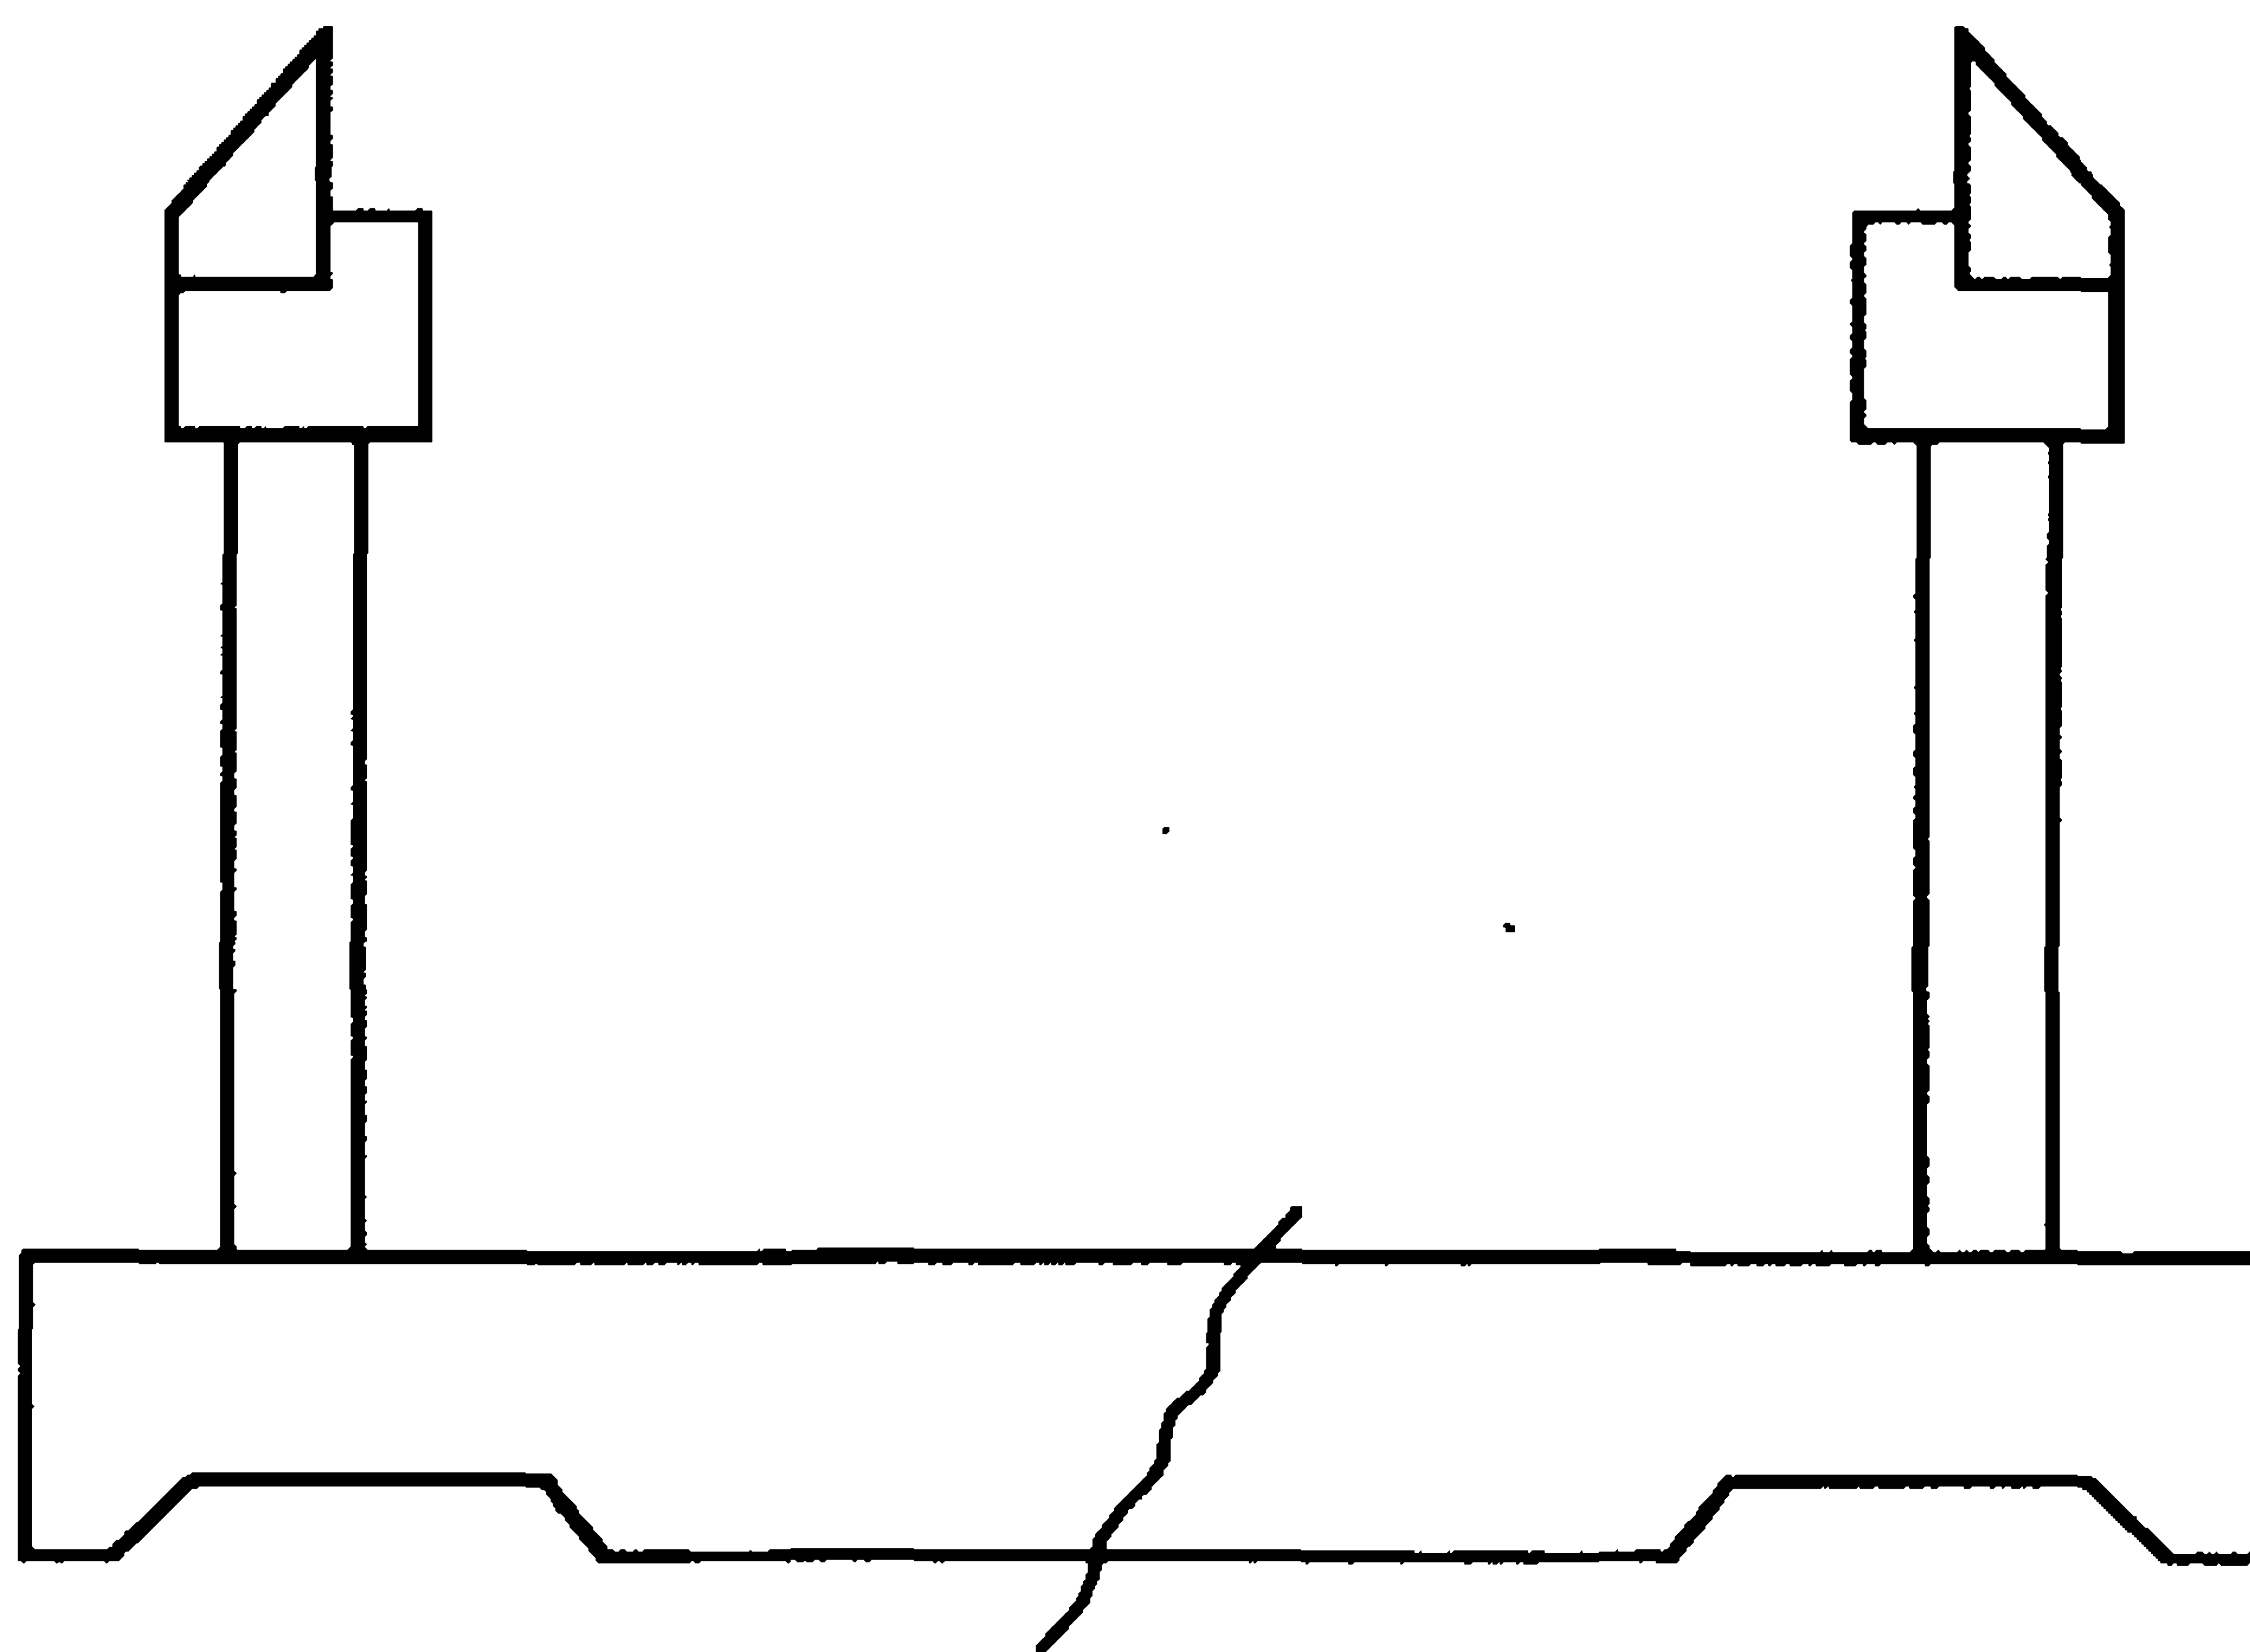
Приспособление для статической балансировки коленчатого вала с маховиком и сцеплением
